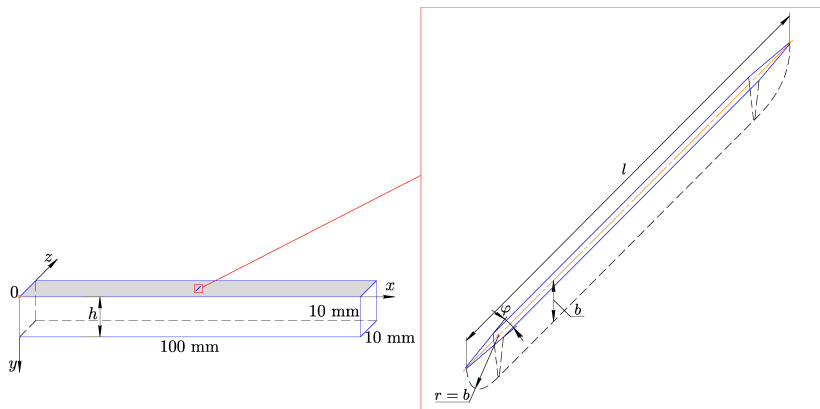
Схематическое изображение поверхностно упрочненного призматического образца с несквозной V-образной трещиной
